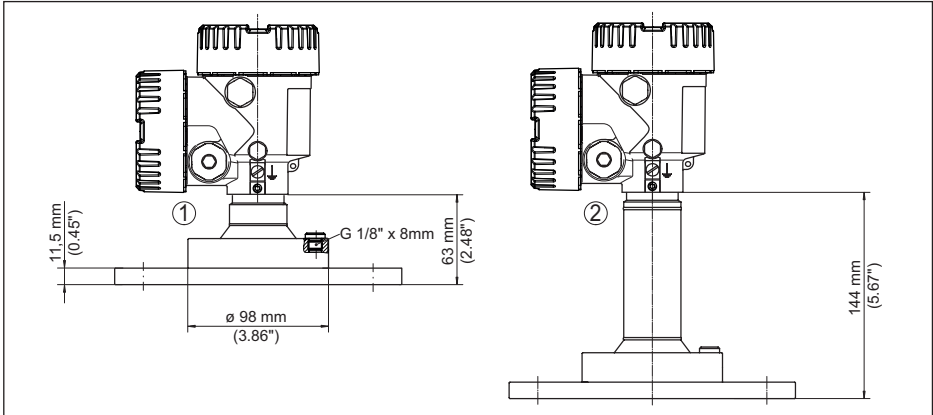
NCR-86, Flansch mit Linsenantenne (Flanschstärke siehe Zeichnung, Flanschmaße nach DIN, ASME, JIS)
